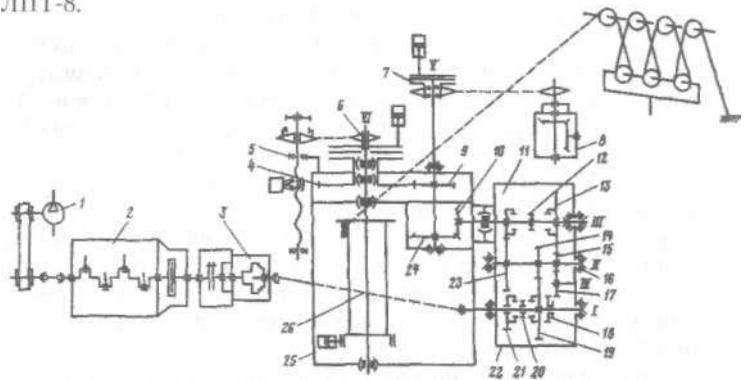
Кинематическая схема установки УПТ1 - 50:
